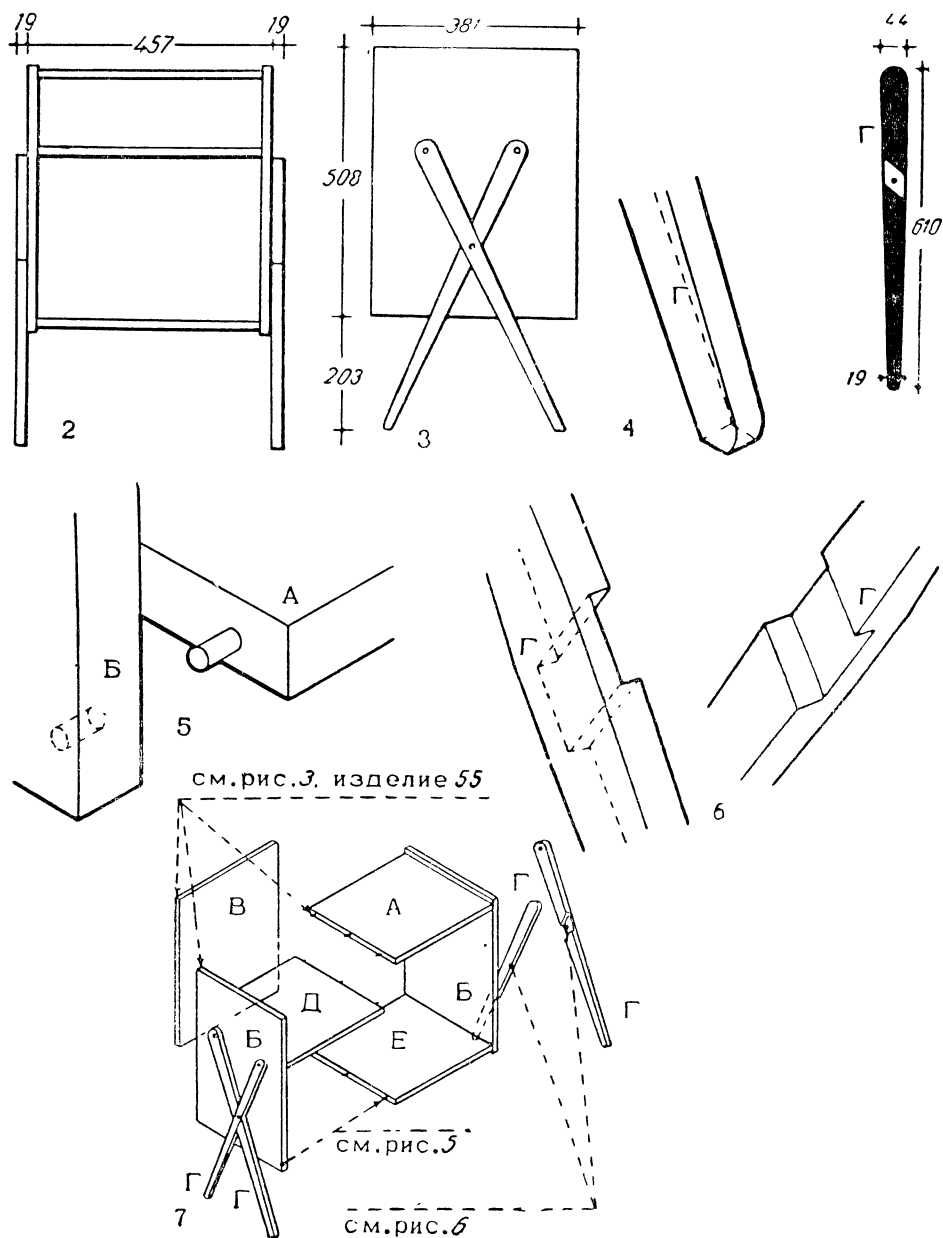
7. 2 — вид спереди; 3 — вид сбоку; 4 — детали ножки; 5 — эскиз соединения нижнего полка с боковой стенкой; 6 — эскиз соединения ножек; 7 — эскиз сборки деталей.
